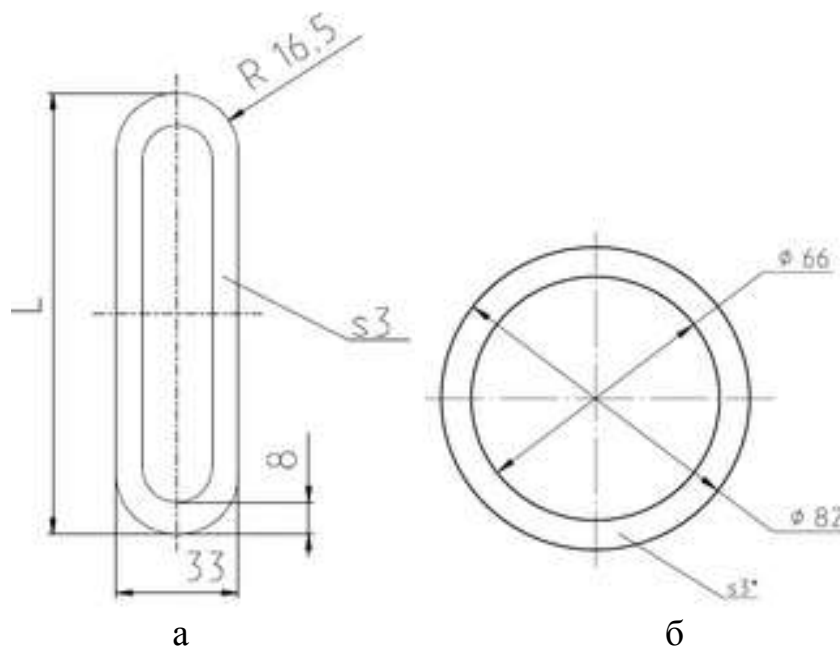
Размеры исходной овальной заготовки (а) и получаемой кольцевой детали (б)
